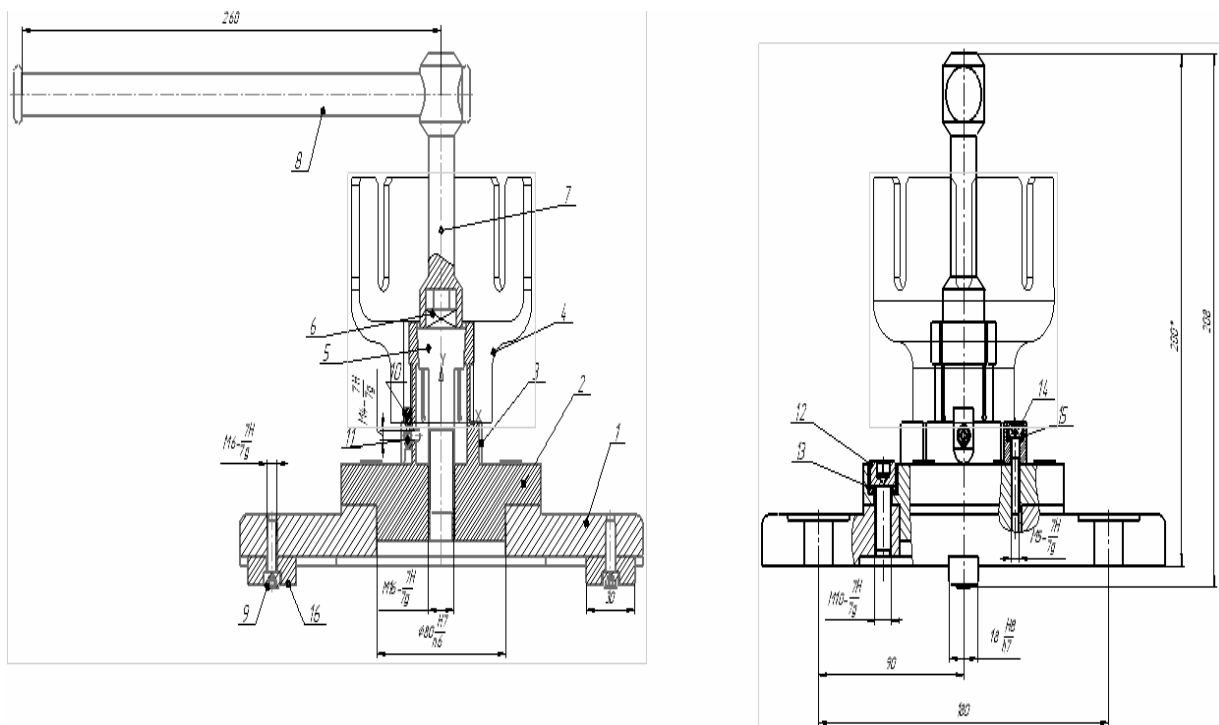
Приспособление для горизонтально-фрезерной с ЧПУ операции
